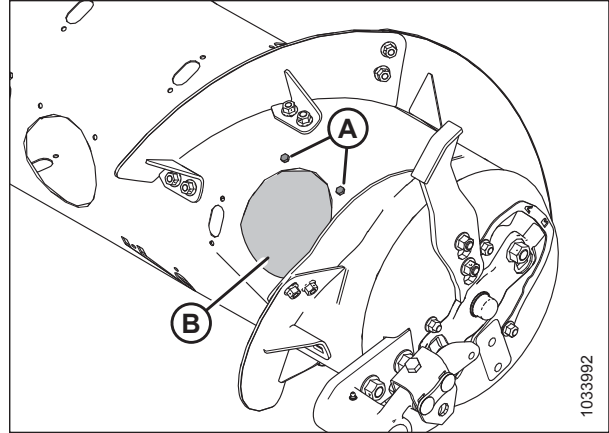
Tampas de acesso do sem fim - Lado direito
